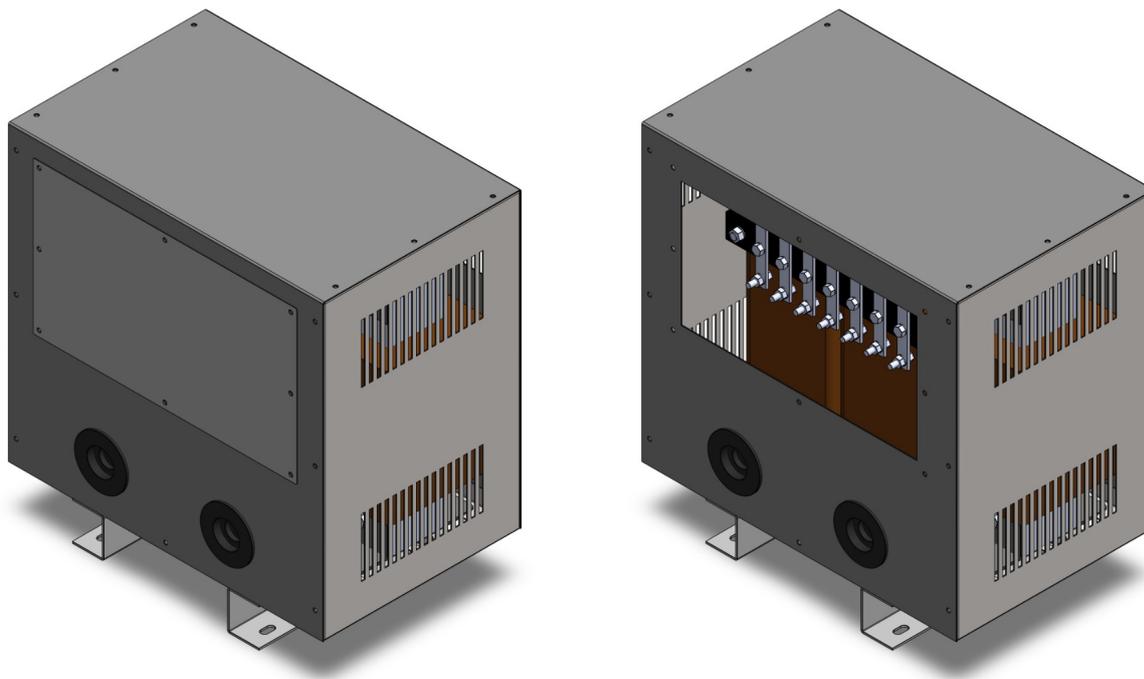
Remover Tampa Frontal - Imagem Ilustrativa.
